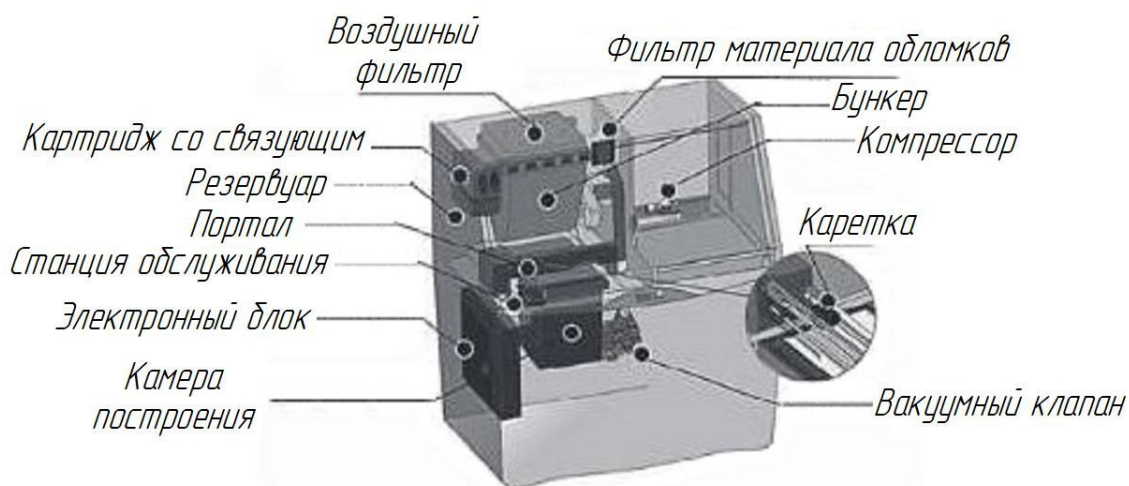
Схема установки ZPrinter® («Z Corp., Inc.»)
